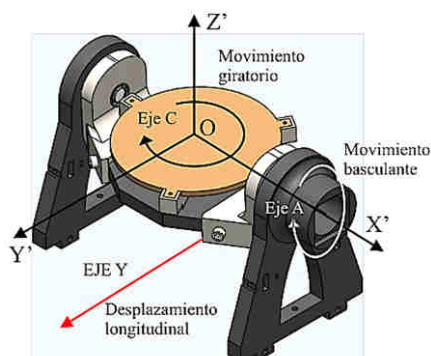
Diseño CAD de Cama de deposición giratoria basculante
